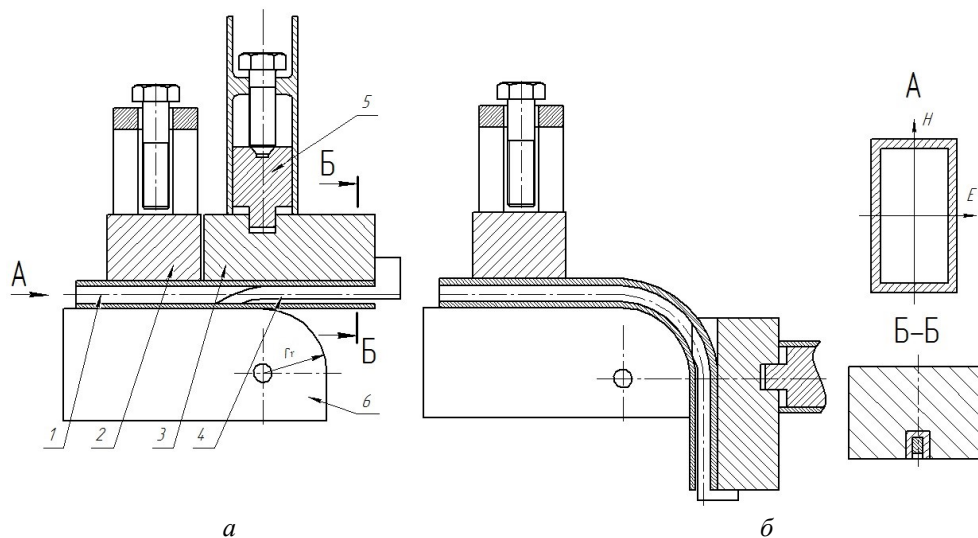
Схема гибки трубы малого сечения с одновременной калибровкой внутреннего сечения: *а* – положение частей приспособления, заготовки и оправки в начальный момент гибки, *б* – положение частей приспособления, заготовки и оправки после гибки; 1 – заготовка, 2 – прижим, 3 – подвижный фиксатор, 4 – калибрующая прямолинейная оправка, 5 – рычаг, 6 – гибочный шаблон
